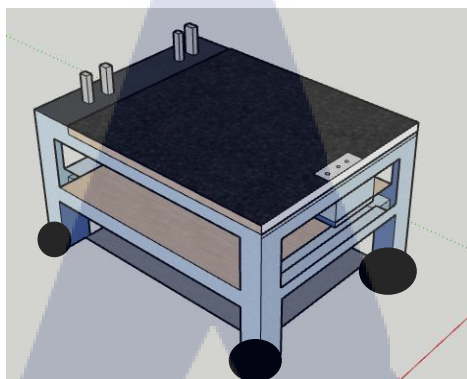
การวางตำแหน่งของ Support table ระหว่าง Gasser machine และ Roll close machine
